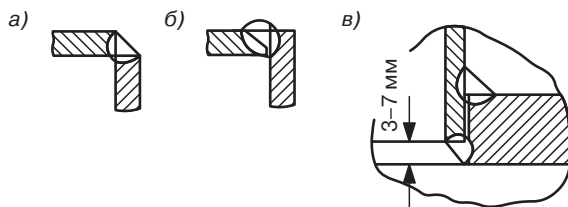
Угловые соединения: а — угловое соединение листов без разделки кромок; б — угловое соединение листов с разделкой одной кромки; в — угловое соединение труб с фланцами
